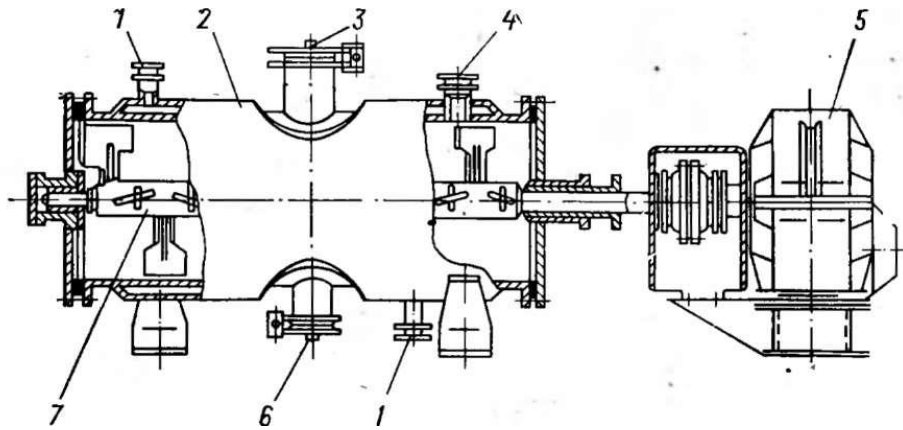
Барабанна вакуумна гребкового сушарка типу СВГР з реверсивним обертанням ротора:
